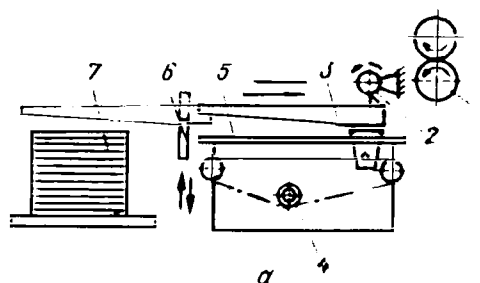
Устройство для механизации сборки пакетов шпона конструкции Жешартского ФК
